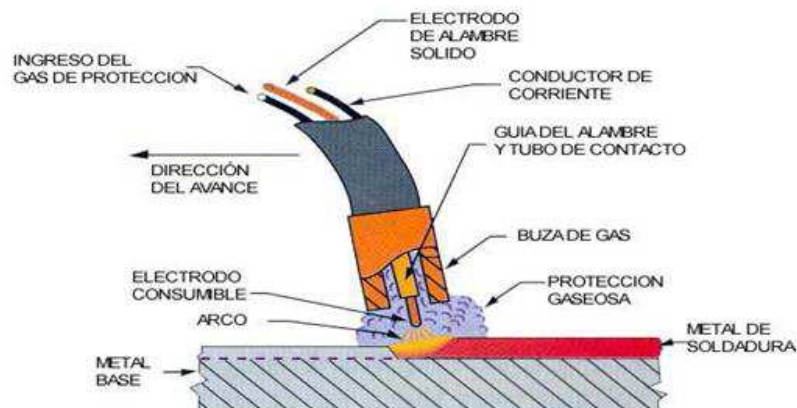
Proceso de soldadura por arco metálico protegido.
